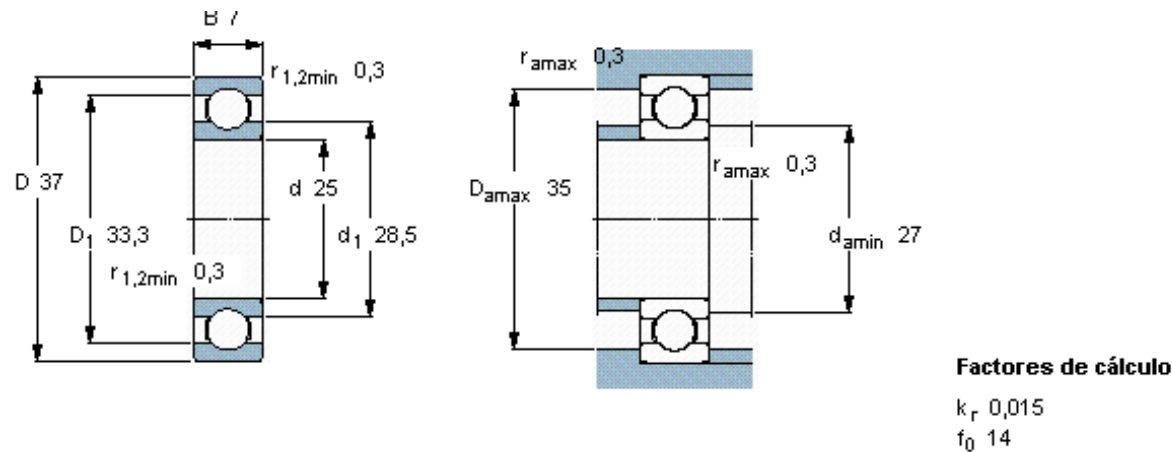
Dimensiones del Rodamiento SKF61805.
